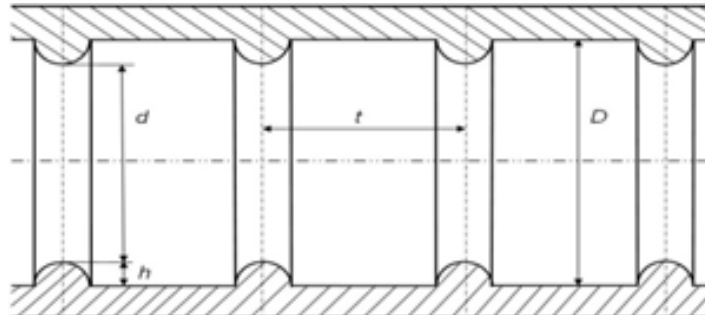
Разрез прямой круглой трубы с поперечными турбулизаторами потока поверхностного расположения полукруглых поперечных профилей
